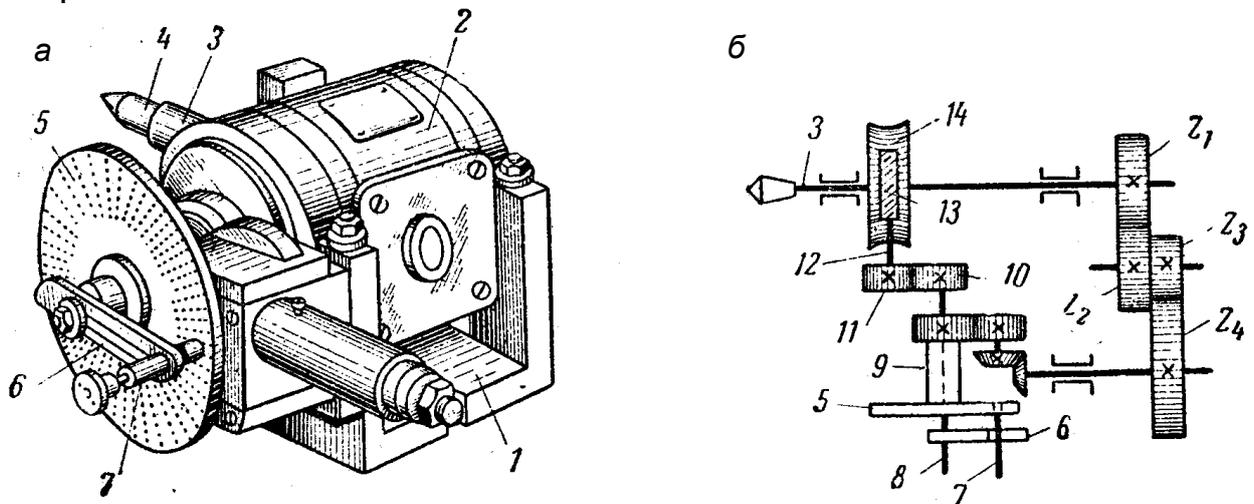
Универсальная делительная головка: а – общий вид; б – кинематиче-
